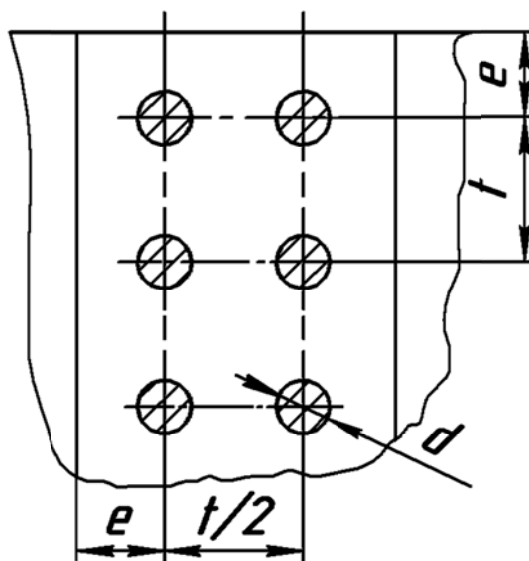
Заклепочный шов цилиндрического автоклава
